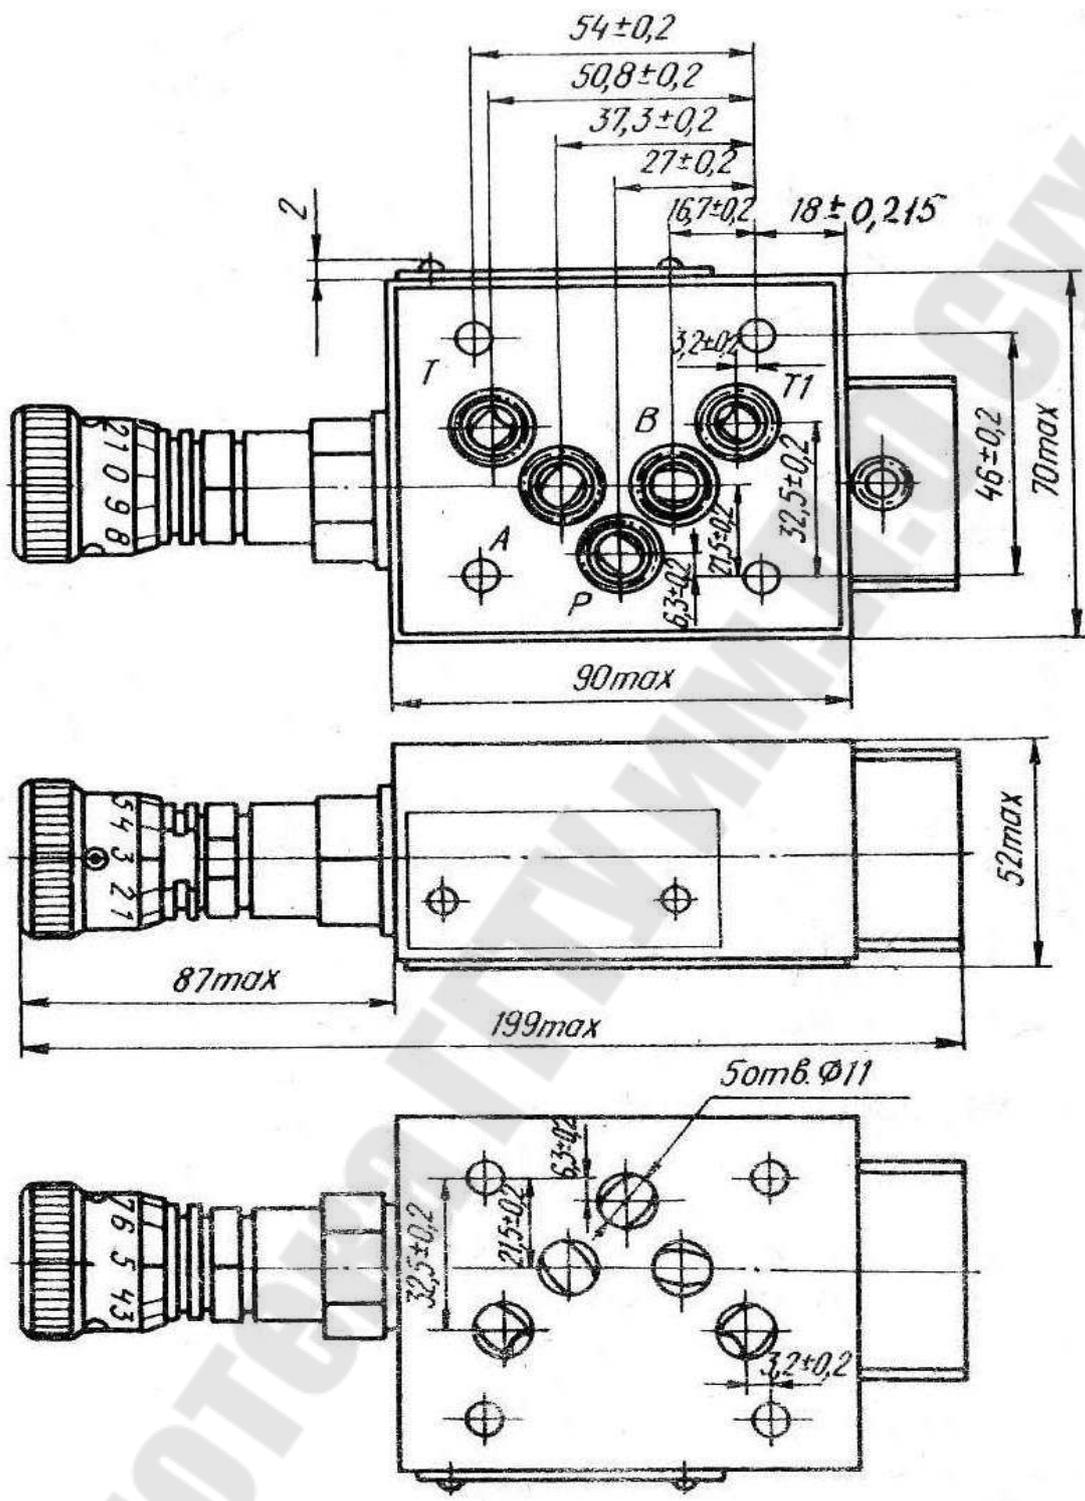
Габаритные и присоединительные размеры регулятора расхода РПМ-102
